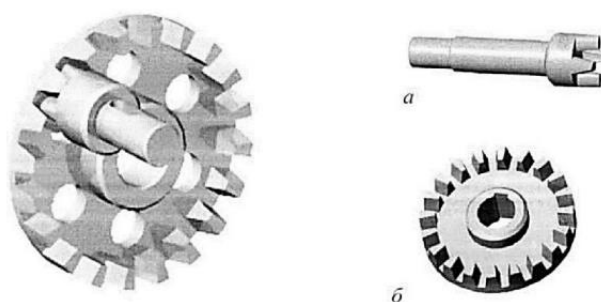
Зубчатая передача с внутренним зацеплением торцевых зубьев и параллельными осями вращения колес [25]
